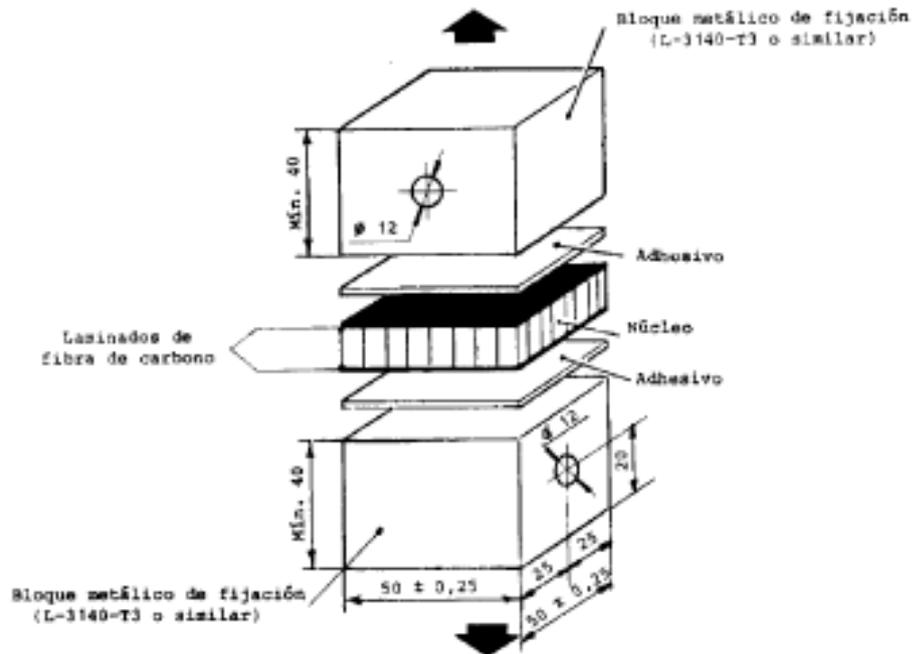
Fijación de las probetas para ensayo de tracción plana.
